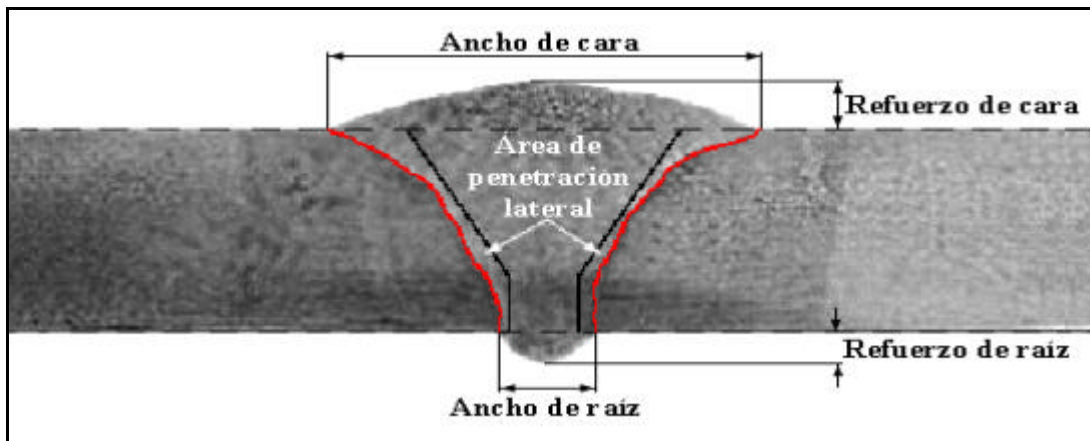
Parámetros geométricos del cordón de soldadura.
